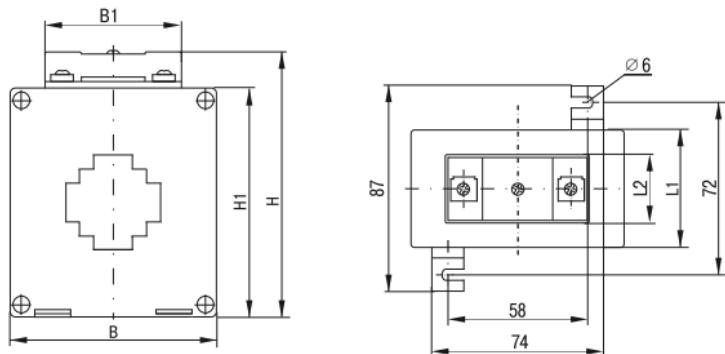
Габаритные и установочные размеры трансформаторов ТОП-0,66
